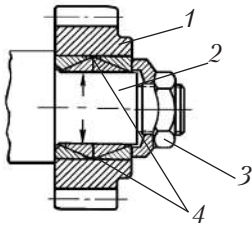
З'єднання з пружинно-затяжними кільцями:
